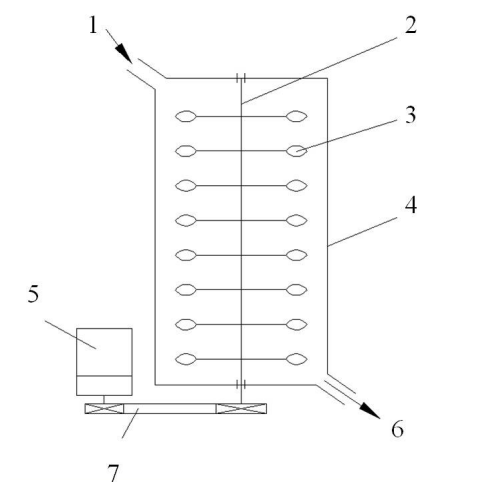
Конструктивная схема роторно-вихревой мельницы: 1 – входной патрубок; 2 – ротор; 3 – била; 4 – корпус; 5 – электродвигатель 6 – разгрузочный патрубок; 7 – клиноременная передача
